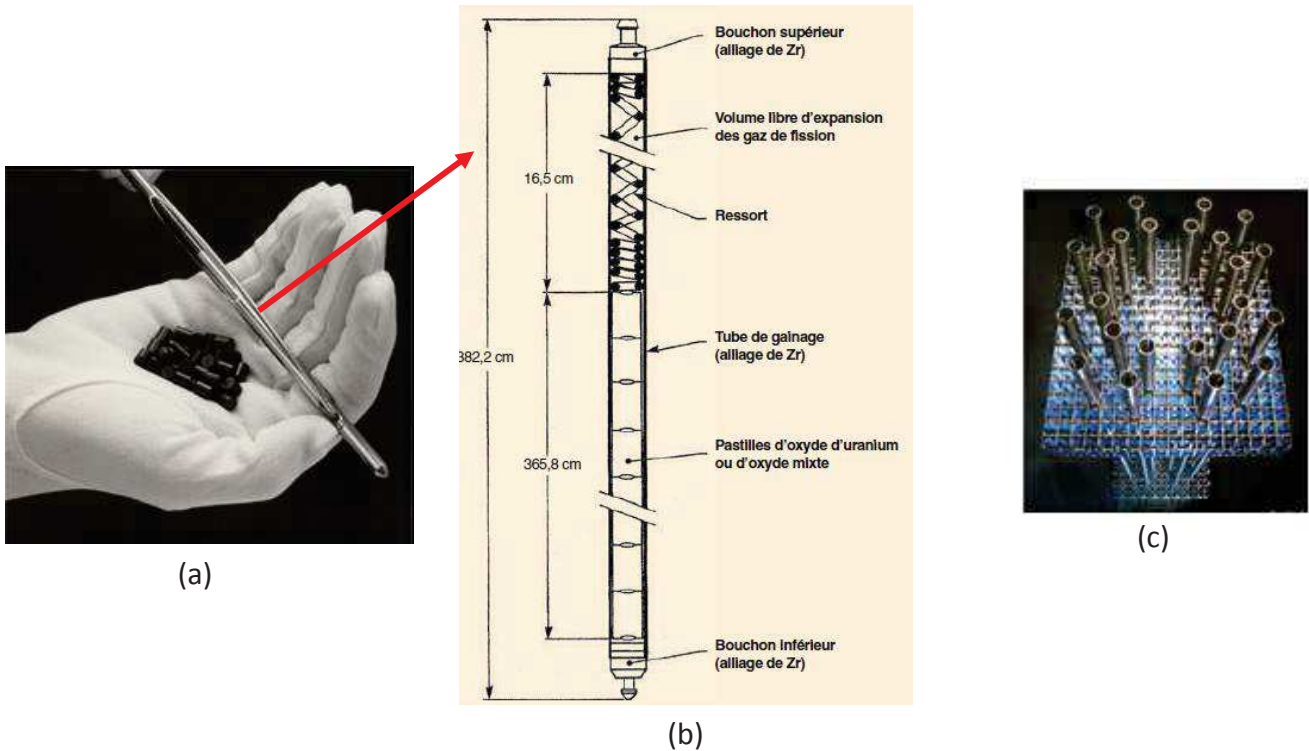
(a) Crayon de combustible nucléaire et pastilles, (b) crayon de combustible et (c) tubes guides et grilles.
